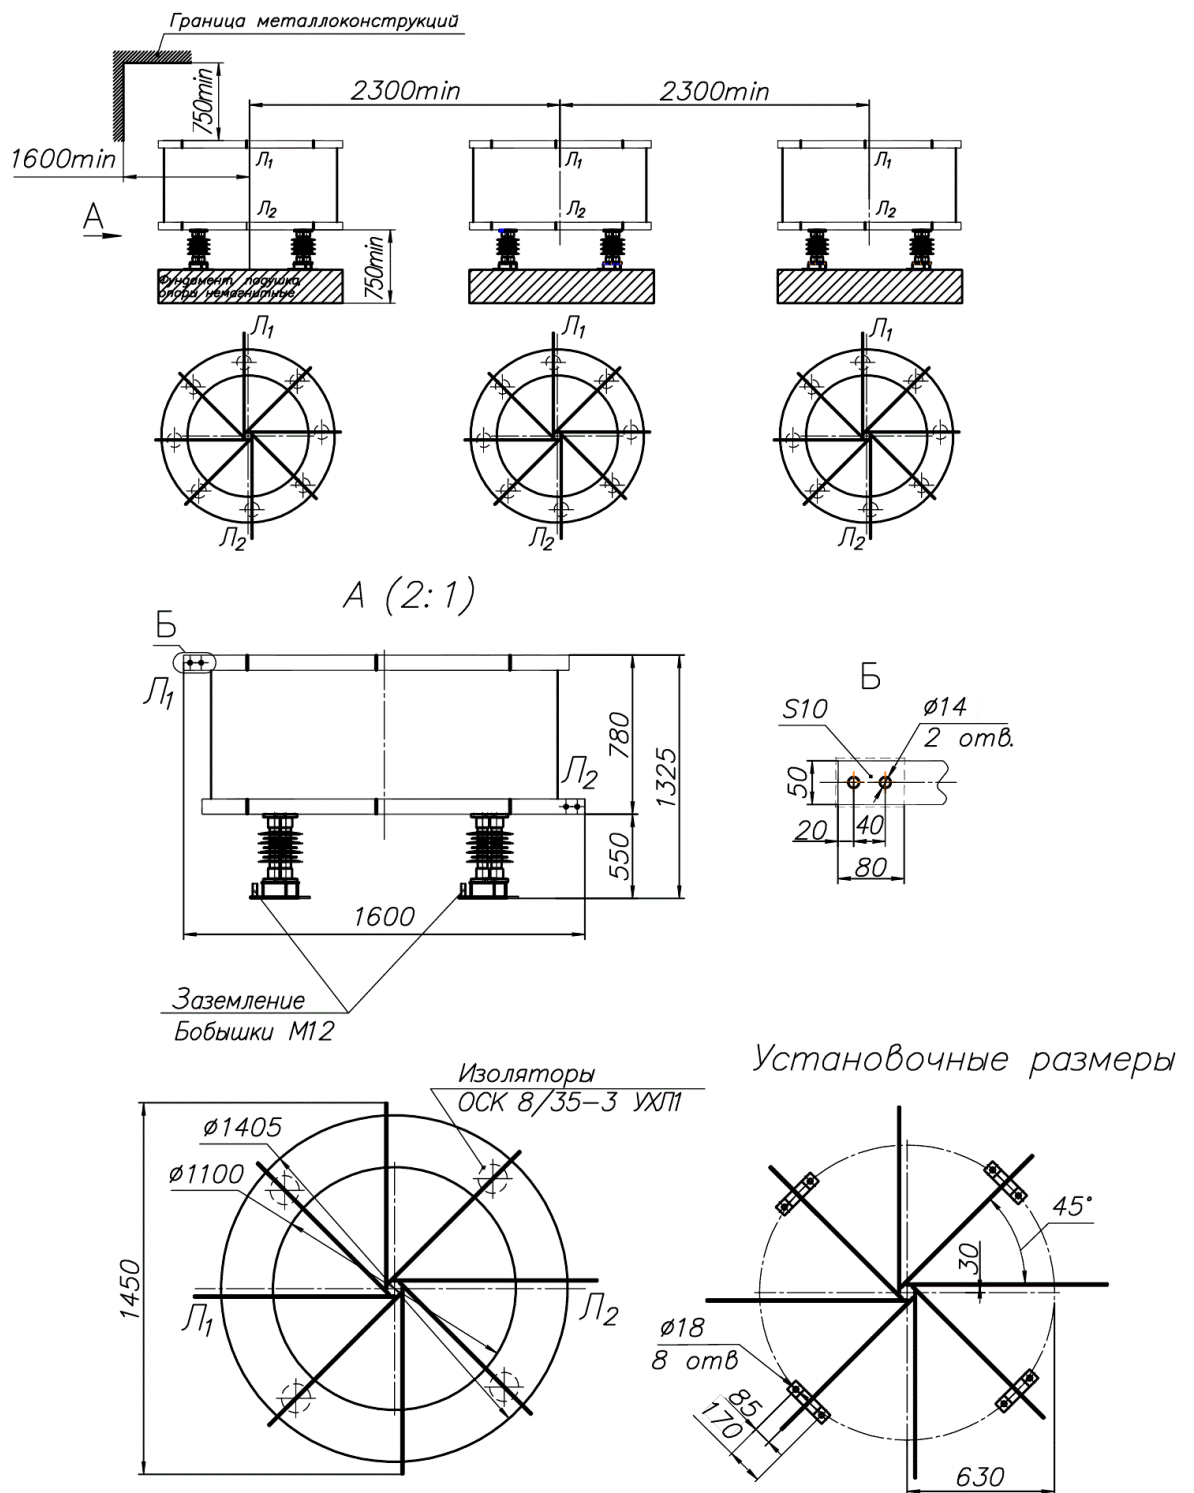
Габаритный чертеж реактора 4,2 мГн, 727 А
